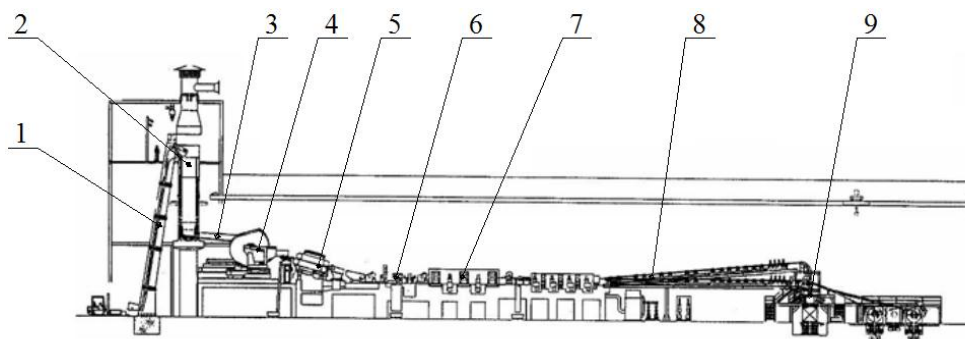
Принципиальная схема установки SMS-MEER: 1 – скиповый подъемник; 2 – плавильная печь; 3 – разливочный желоб; 4 – раздаточная печь; 5 – машина непрерывного литья; 6 – машина подготовки; 7 – прокатный стан; 8 – машина окончательной обработки; 9 – моталка
